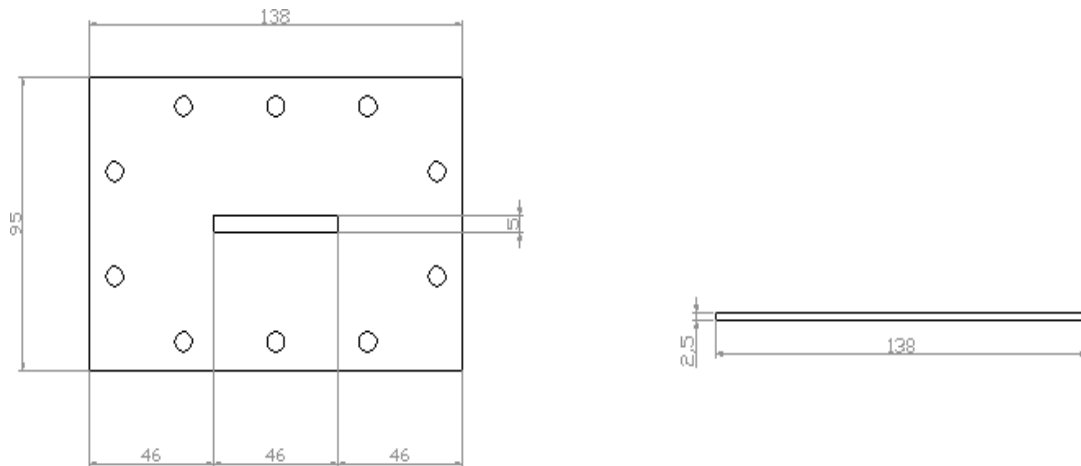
Disegni tecnici dell'applicatore costruito: vista frontale della flangia con la fessura (a sinistra) e spessore della flangia (a destra) con le principali dimensioni (in mm).
